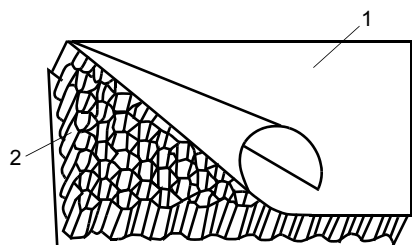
Типовая конструкция сотовой панели: 1 — обшивка; 2 — сотовый наполнитель
